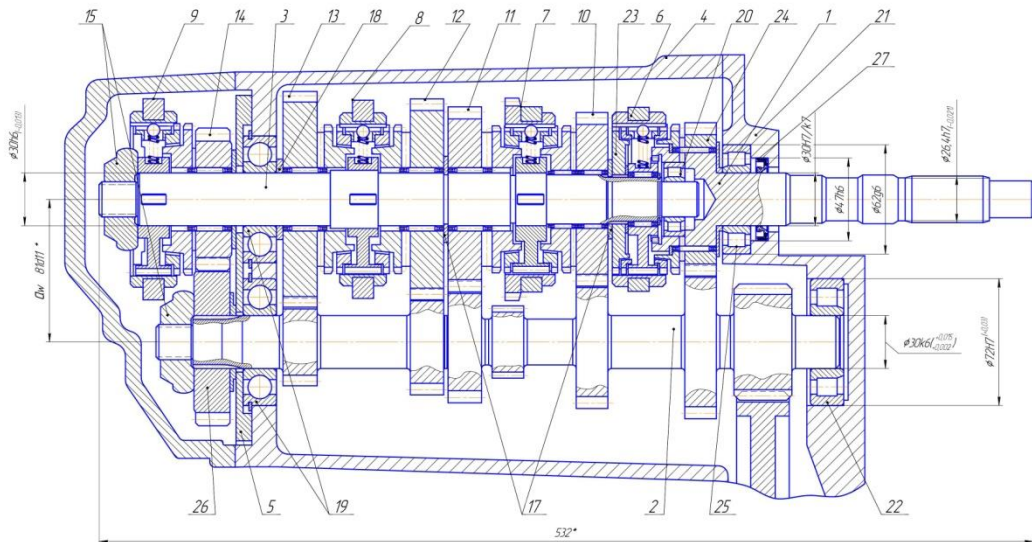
Складальний кресленик розробленої трьохвальної коробки передач
